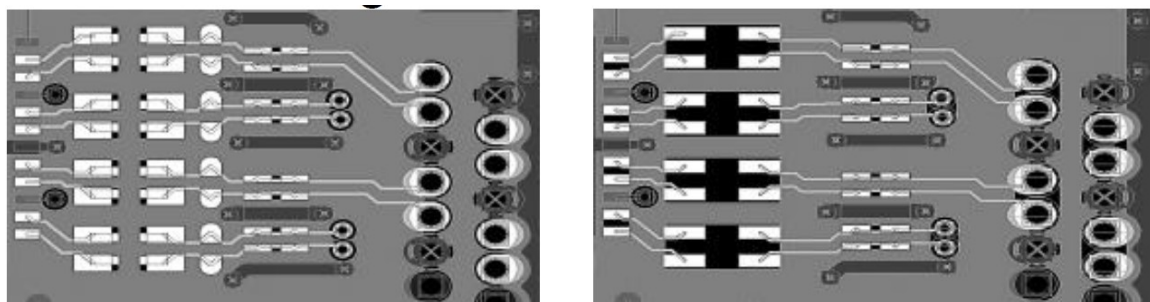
原始 layout (左圖) & 最佳化 layout (右圖)
